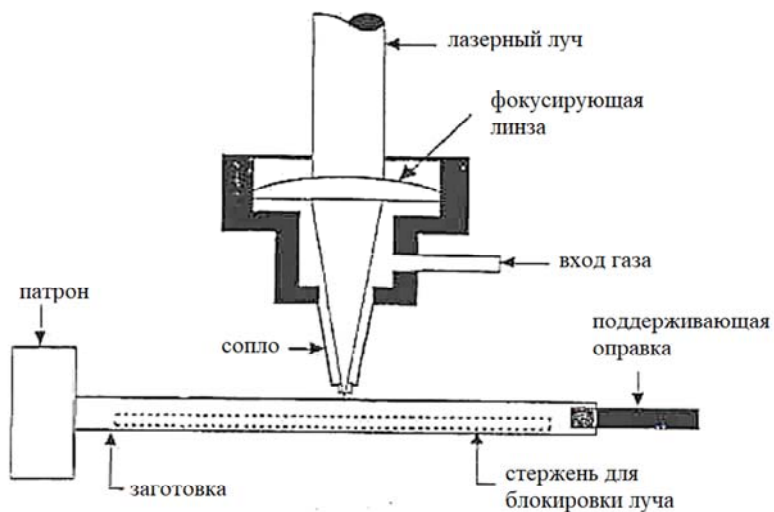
Схема установки лазерной резки заготовок матричных стентов
